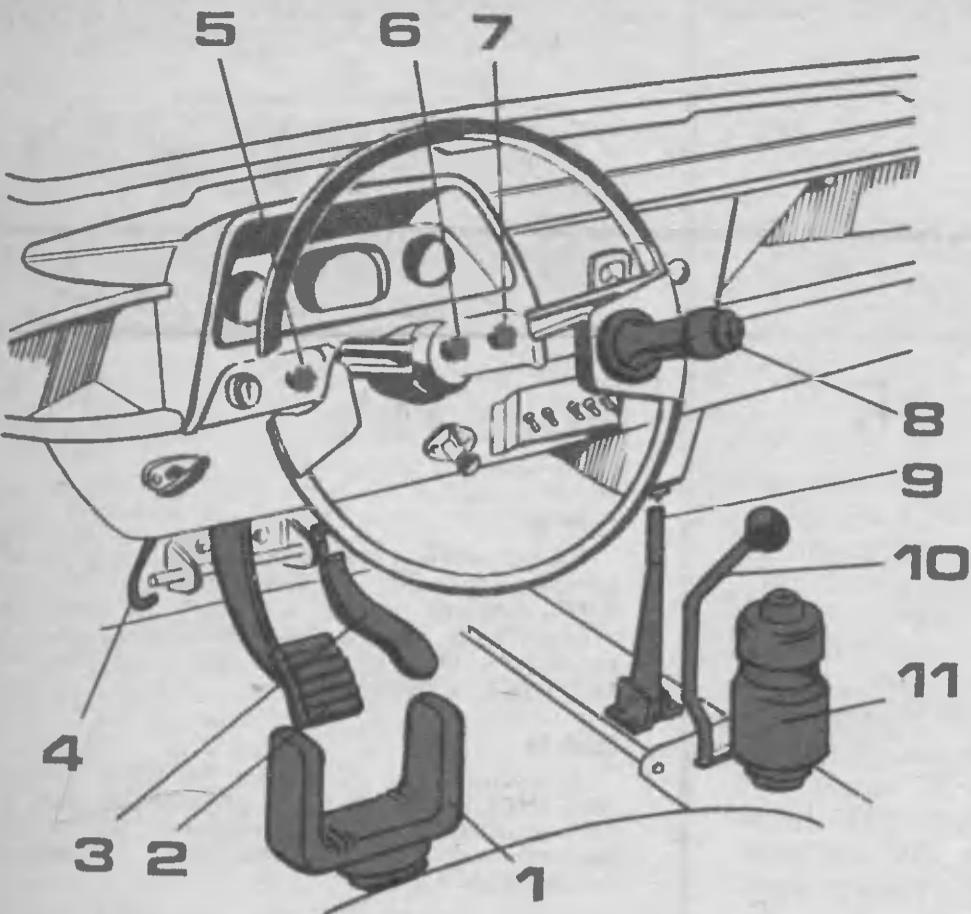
Органы управления ЗАЗ-968Р: 1 — вилка рычага переключения передач; 2 — педаль тормоза; 3 — педаль «газа»; 4 — педаль привода стеклоомывателя; 5 — выключатель стеклоочистителя; 6 — переключатель света; 7 — выключатель отопителя; 8 — рукоятка управления; 9 — рычаг стояночного тормоза; 10 — рычаг включения заднего хода; 11 — тяговое реле выбора III передачи.
